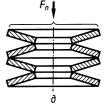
Схемы сборки пружин в пакеты:
